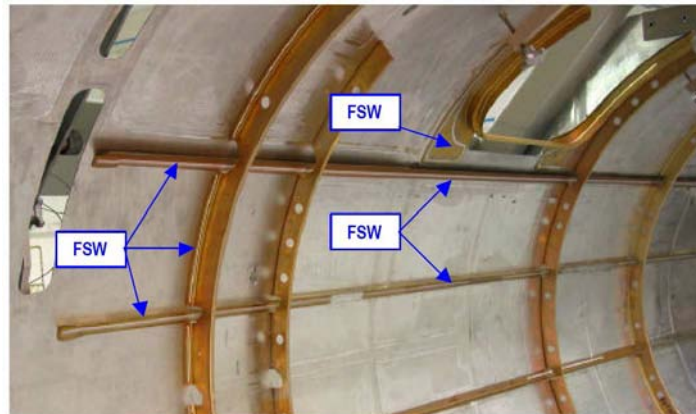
Painel integral direito da fuselagem do primeiro protótipo de Eclipse 500 unidas por “Friction Stir Welding – FSW” [Eclipse, 2007].
